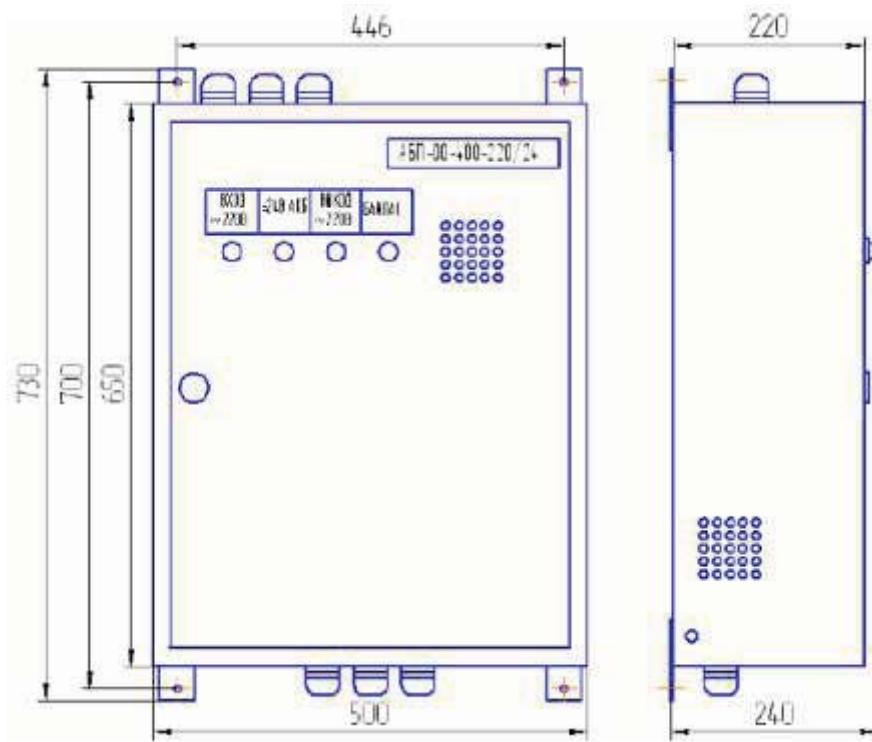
Габаритный чертёж АБП-ОО-400-220/24
